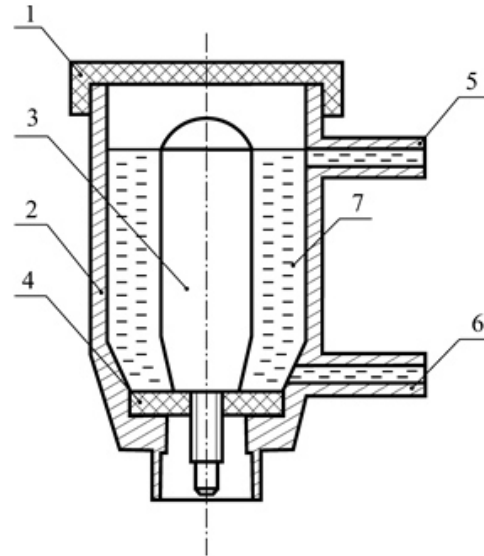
Измерительный проточный коаксиальный преобразователь: 1 — крышка; 2 — корпус; 3 — электрод; 4 — изоляционная шайба; 5 — входной трубчатый канал; 6 — выходной трубчатый канал; 7 — трансформаторное масло
